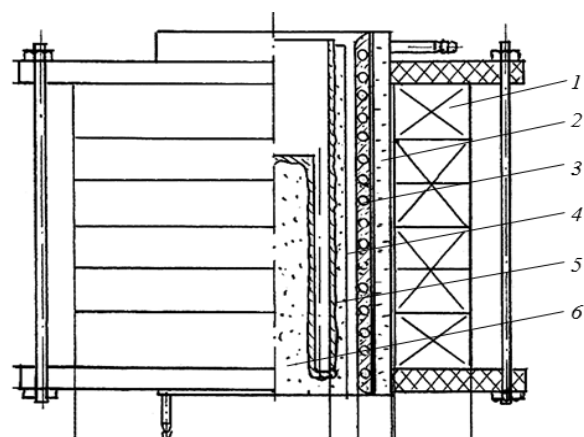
Двухполюсный цилиндрический электромагнитный индуктор:
